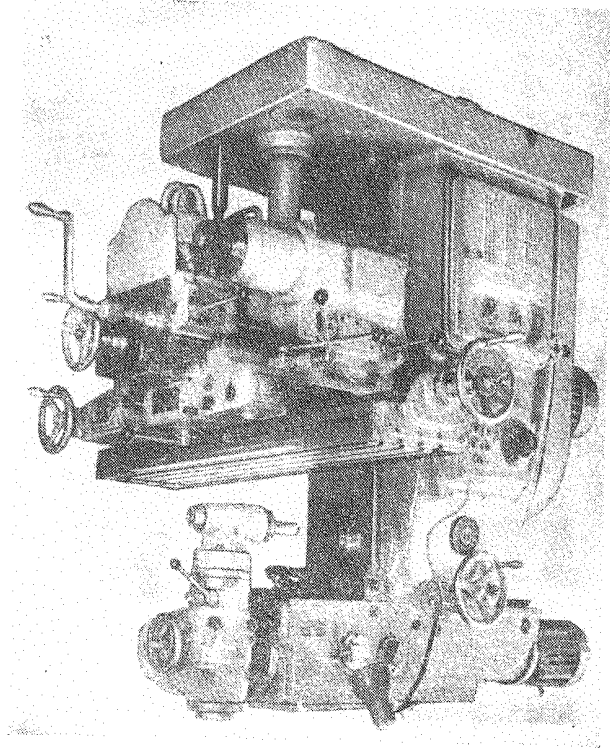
Широкоуниверсальный консольно-фрезерный станок модели 6М82П
